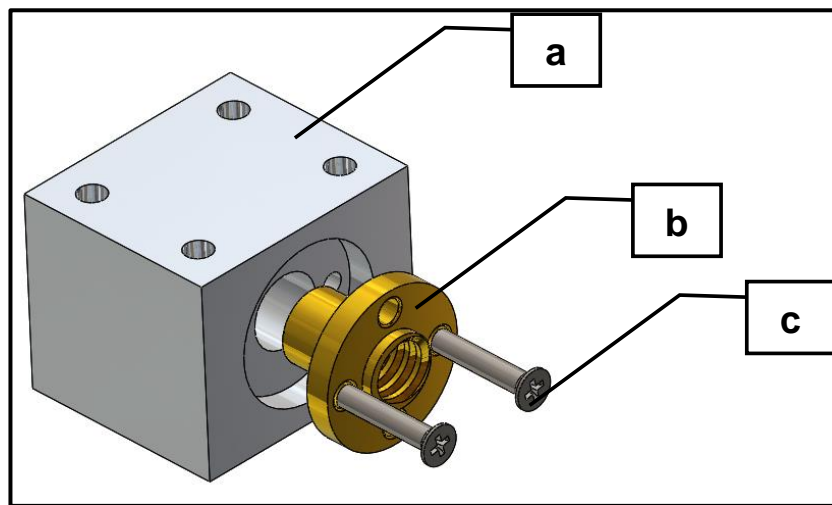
Ensamblaje de bloque de aluminio y tuerca de bronce M8 para el eje Z
